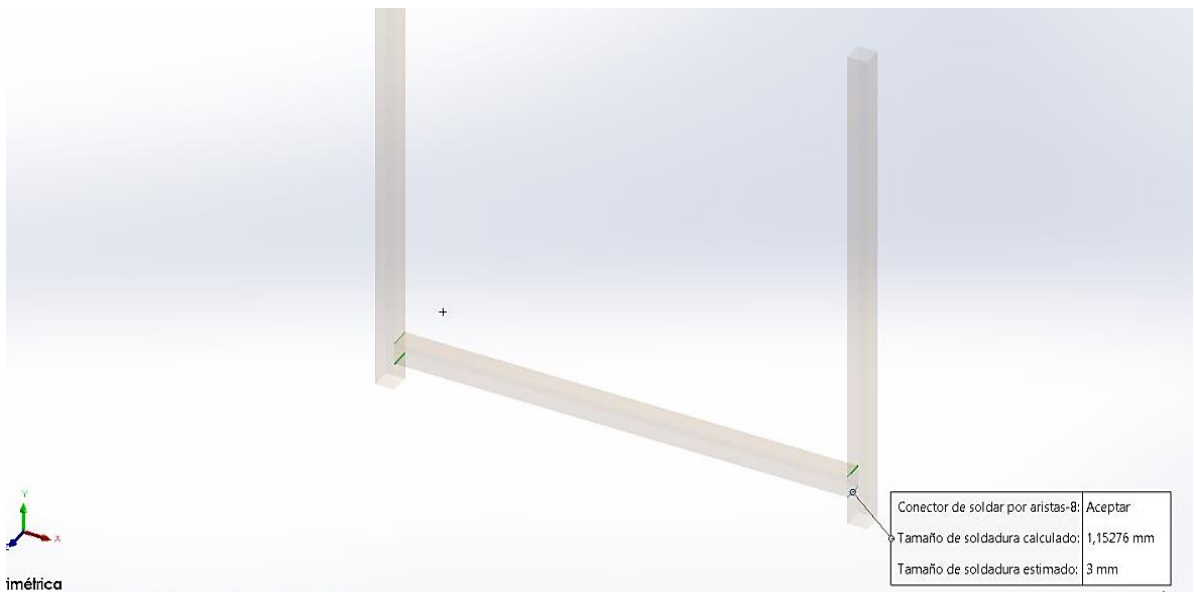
Tamaño de soldadura en uno de los conectores.
